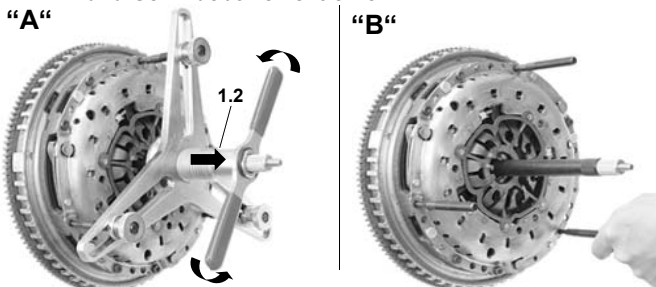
Kupplungs-Zentrierwerkzeug bzw. -Zentrierdorne herausnehmen.
